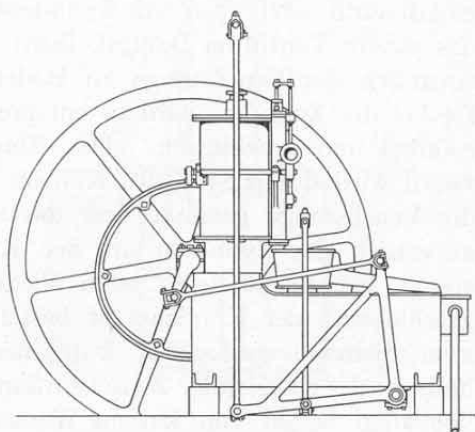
Dampfmaschine mit Winkelhebel in Soho, erbaut 1802.
